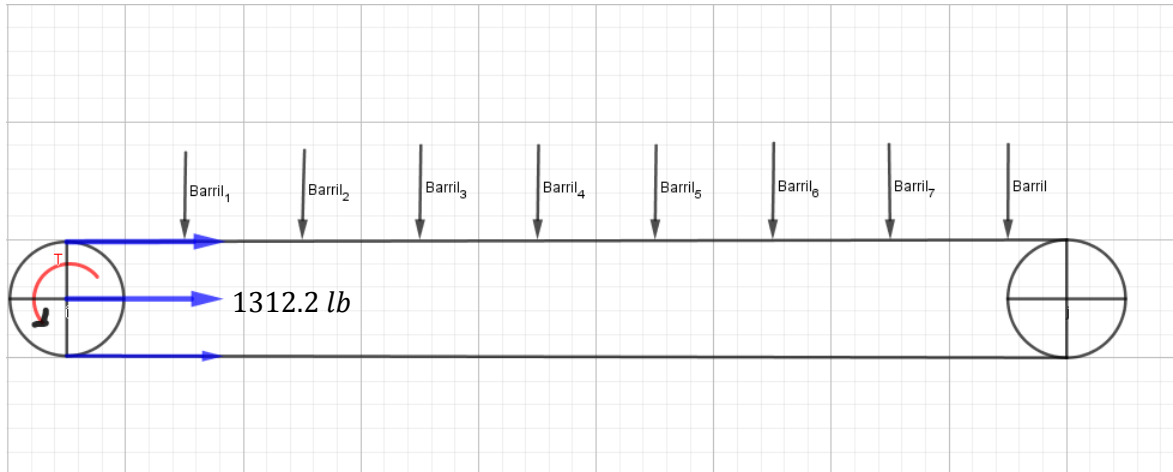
Posición de los barriles aplicando la fuerza de arrastre.
